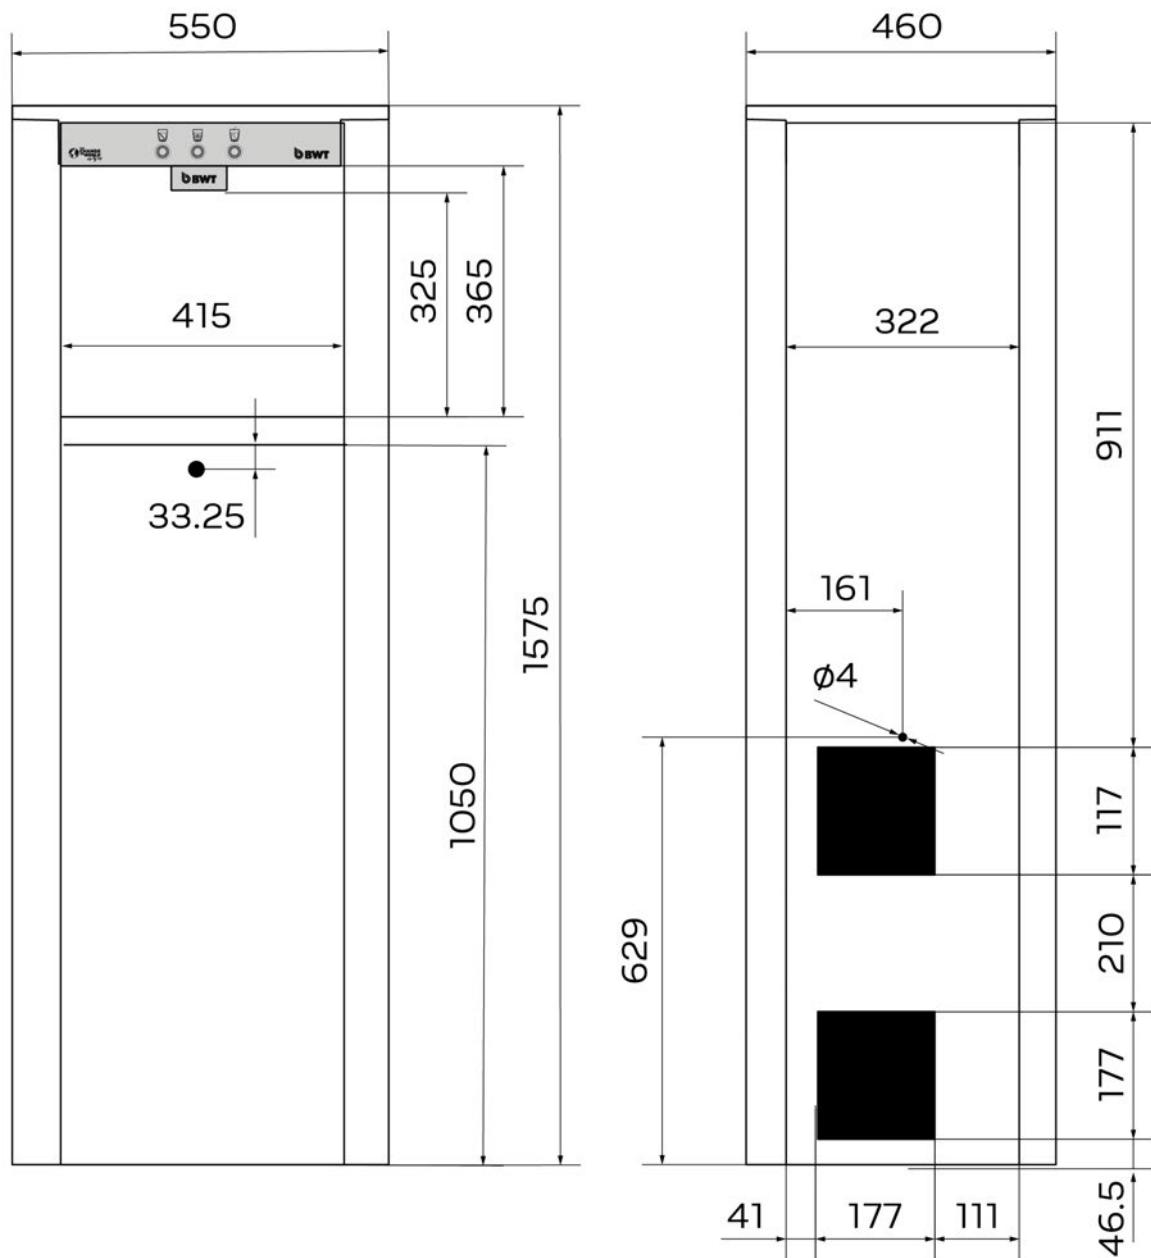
Abmessungen und Dimensionen BWT AQA drink Pro 3 in Millimeter
